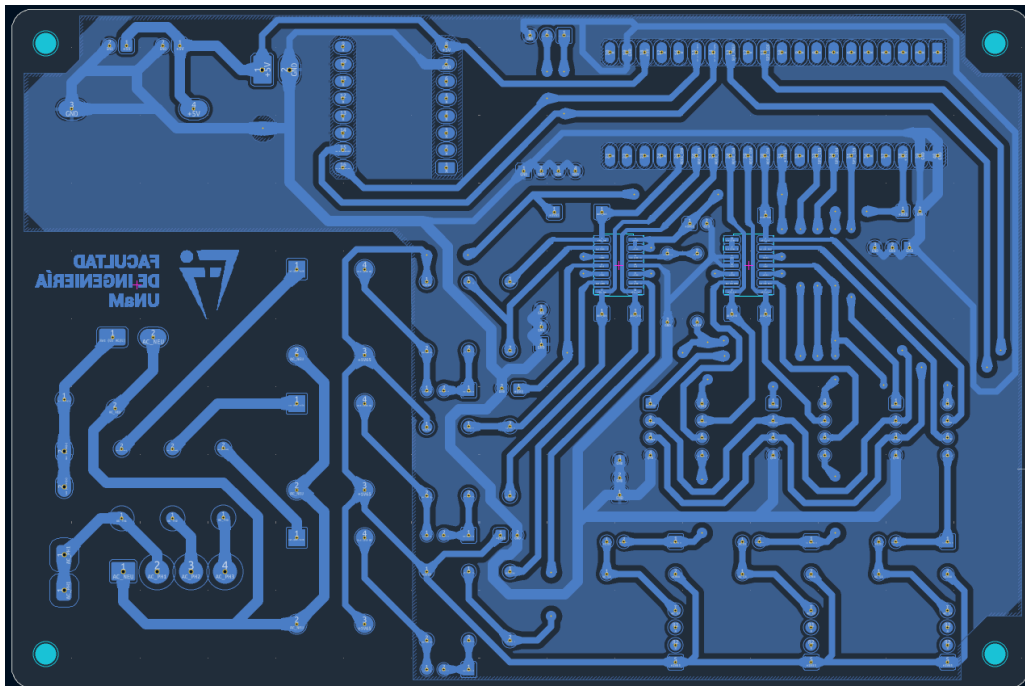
Ruteado de la capa inferior (Bottom Layer) de la PCB.
